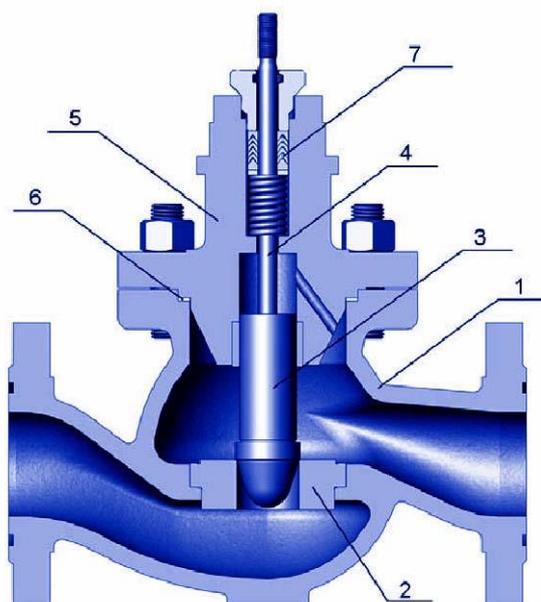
Конструкция регулирующего клапана, где: 1 – корпус; 2 – седло; 3 – плунжер; 4 – шток; 5 – крышка клапана; 6 – уплотнительная прокладка; 7 – сальниковый узел
